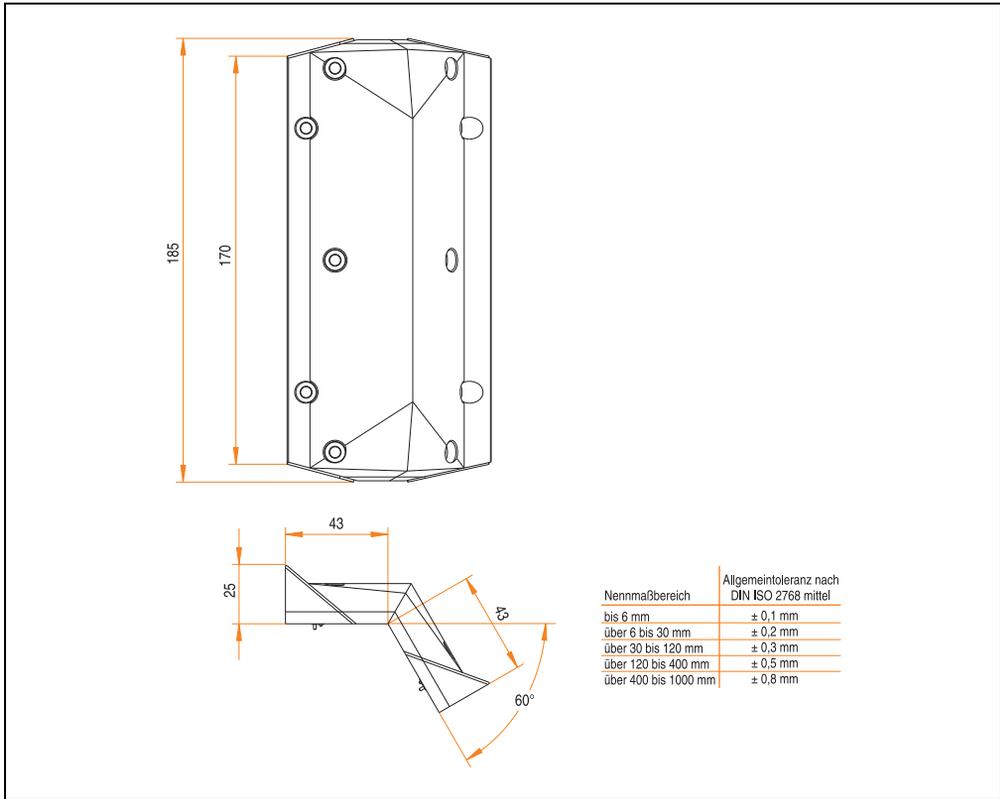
Abmessungen Extension Connector 60° 5AC800.CON2-00
